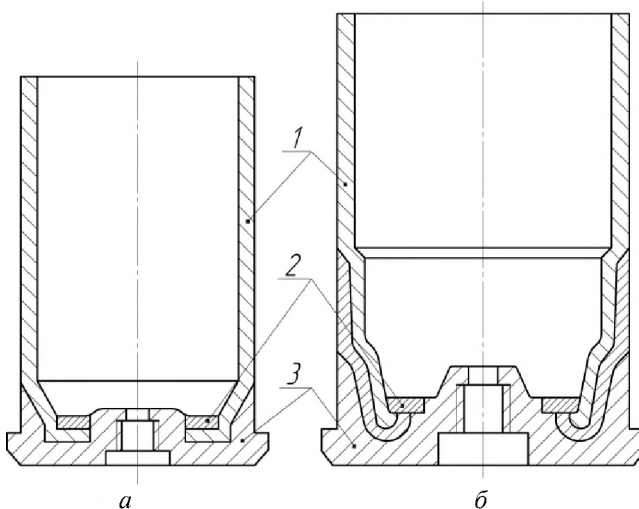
Сборные артиллерийские гильзы: *а* – цельнокорпусная; *б* – со свертным корпусом: 1 – корпус; 2 – соединительное кольцо; 3 – дно
